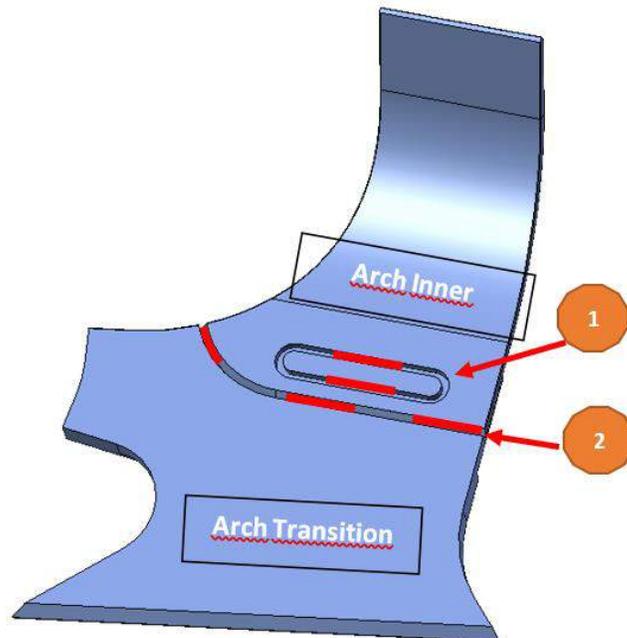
Buena práctica de alternar áreas de soldado
